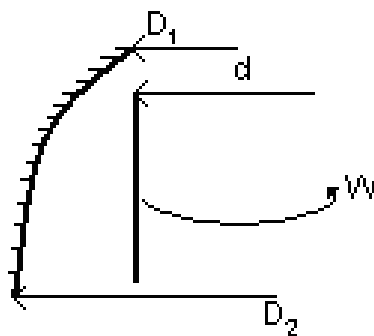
Конструкція з параболічною формою твірної кожуха та циліндричною формою твірної шнека
